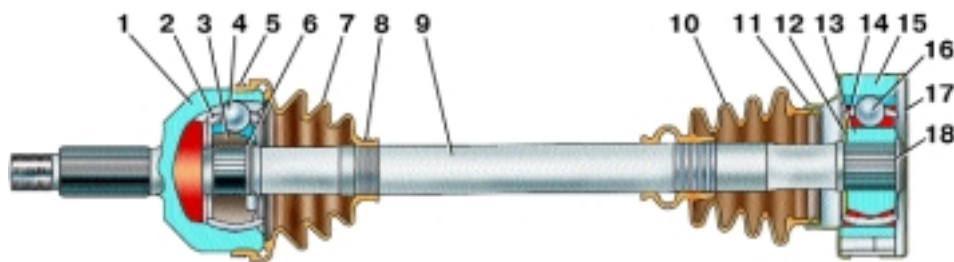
Привод переднего колеса фирмы GKN (Германия): 1 – корпус наружного шарнира; 2 – сепаратор наружного шарнира; 3 – обойма наружного шарнира; 4 – шарики наружного шарнира; 5 – хомут чехла наружного шарнира; 6 – запорное кольцо наружного шарнира; 7 – чехол наружного шарнира; 8 – малый хомут чехла наружного шарнира; 9 – вал привода колеса; 10 – чехол внутреннего шарнира; 11 – чехлодержатель; 12 – упорное кольцо внутреннего шарнира; 13 – обойма внутреннего шарнира; 14 – сепаратор внутреннего шарнира; 15 – корпус внутреннего шарнира; 16 – шарики внутреннего шарнира; 17 – транспортная крышка внутреннего шарнира; 18 – запорное кольцо внутреннего шарнира
